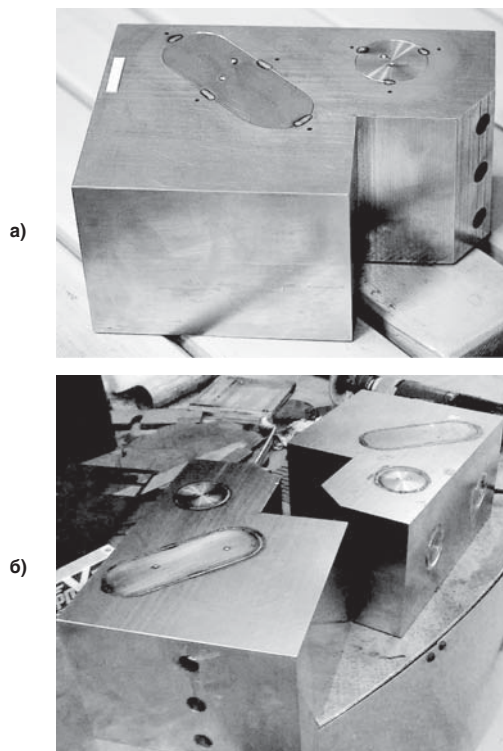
Коллектора внешней отражающей мишени ЦСД после сборки и постановки прихваток (а), после лазерной сварки (б).
